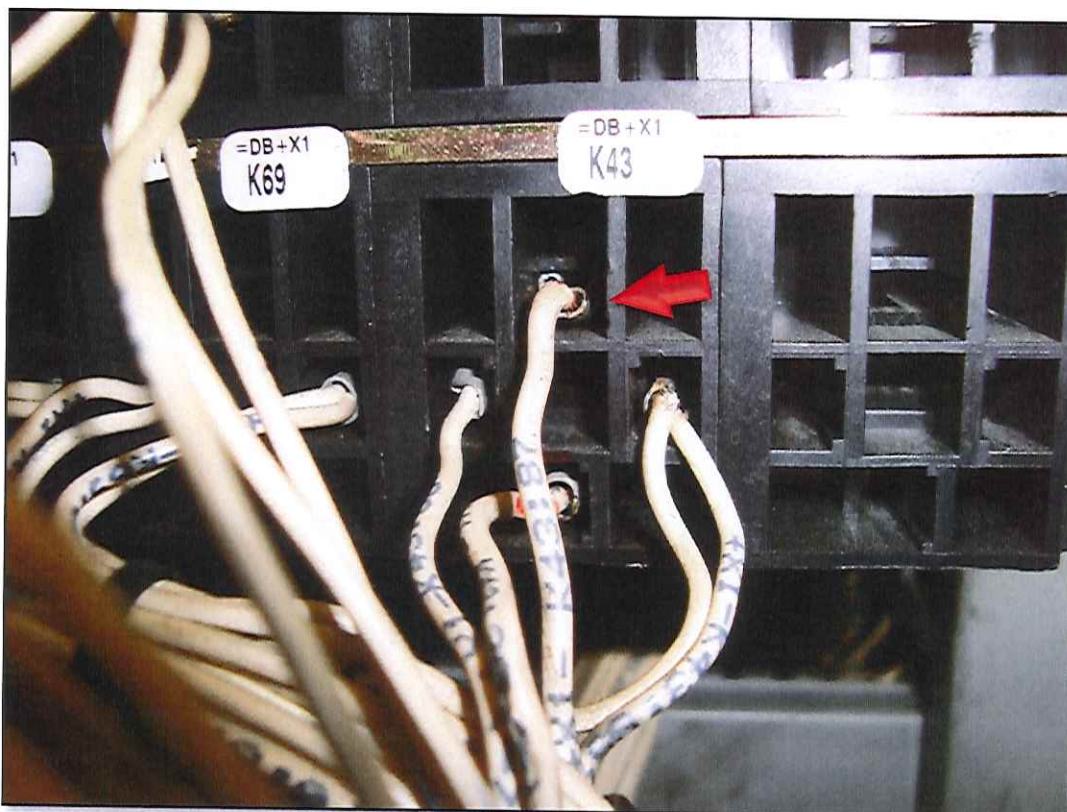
Detalhe do item de check-list #39; cabo do disjuntor K43 apresenta oxidação.
